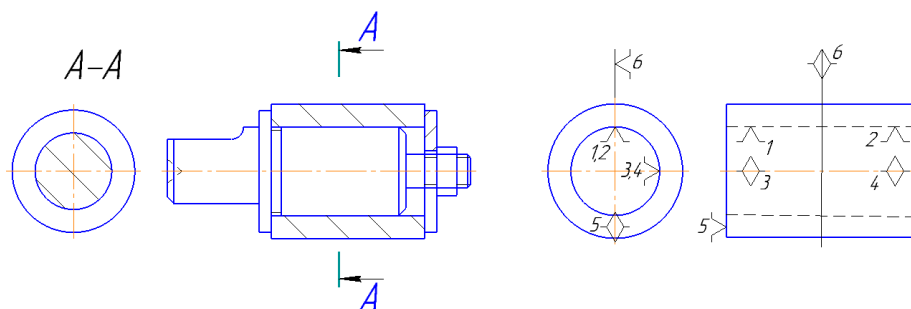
Установка втулки на цилиндрической оправке (с зазором): 1–6 – опорные точки
